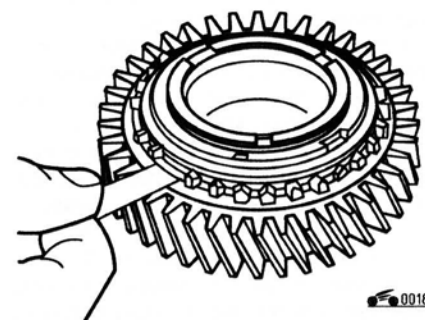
Проверка внешнего кольца синхронизатора II передачи
